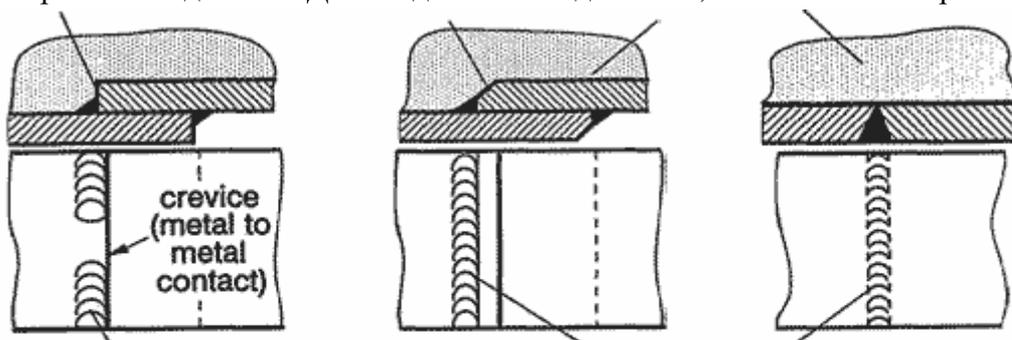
Сварное соединение. (а) соединение внахлестку с прерывистым (точечным) швом, в области стыка между швами создаются щели; (б) улучшенный вариант соединения внахлестку с непрерывным швом и сточенной кромкой листа; (с) правильный способ, стыковое соединение характеризуется гладкой поверхностью и непрерывным сварным швом.
